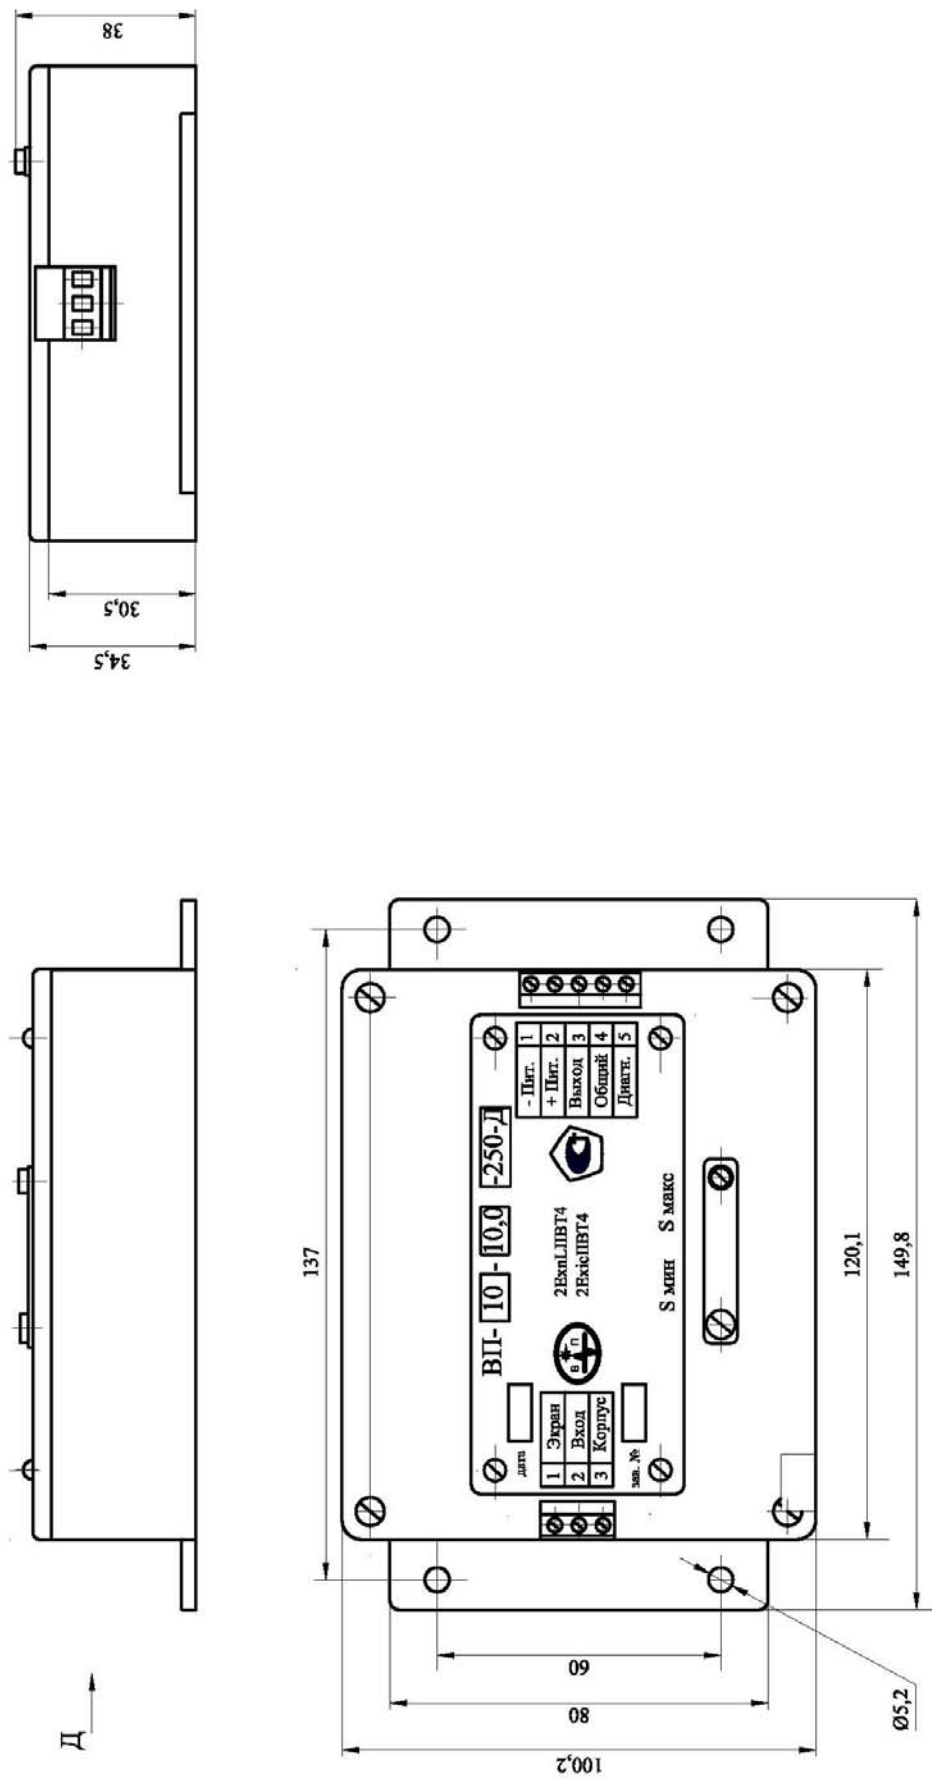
Габаритно-установочные размеры генератора-преобразователя ВП-10-10,0-250-Д
